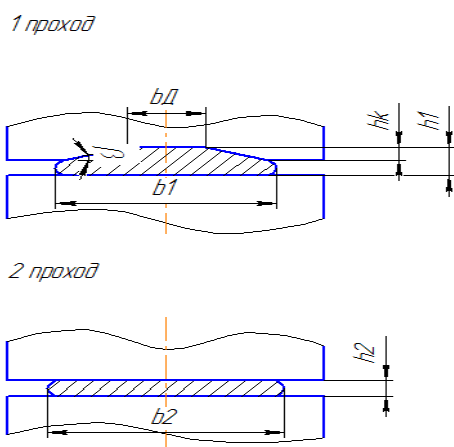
Прокатка рессорной заготовки в два прохода
